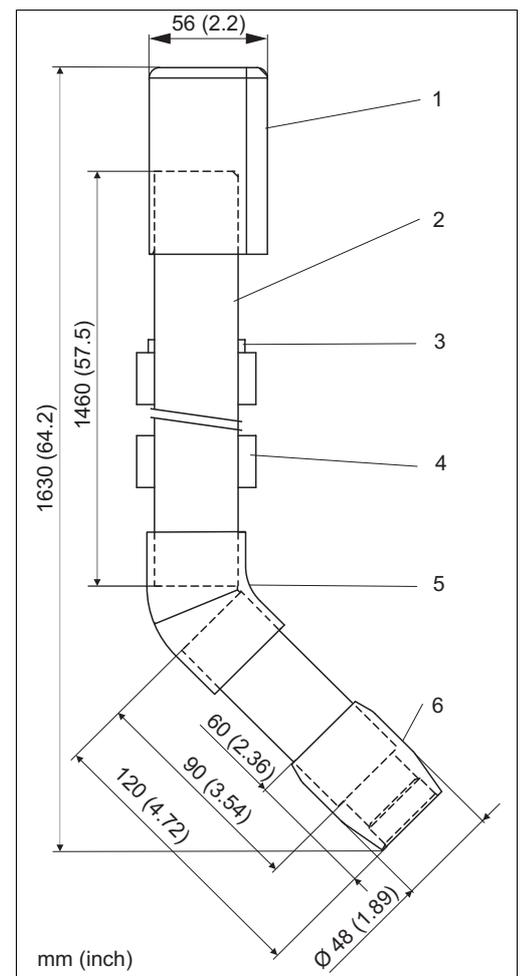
Abmessungen CYA611-\*E (45° gekrümmt)
